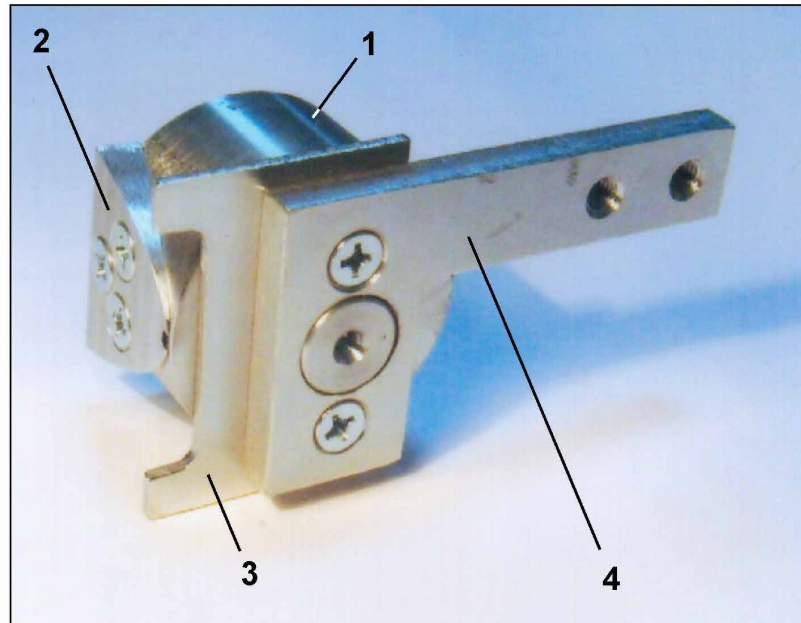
Інструментальна головка пристрою для обробки електричною дугою тіл обертання дротовим електрод-інструментом: 1 – тримач дроту; 2 – планка для створення кумулятивного потоку; 3 – напрямляч дроту; 4 – тримач, що приєднує
